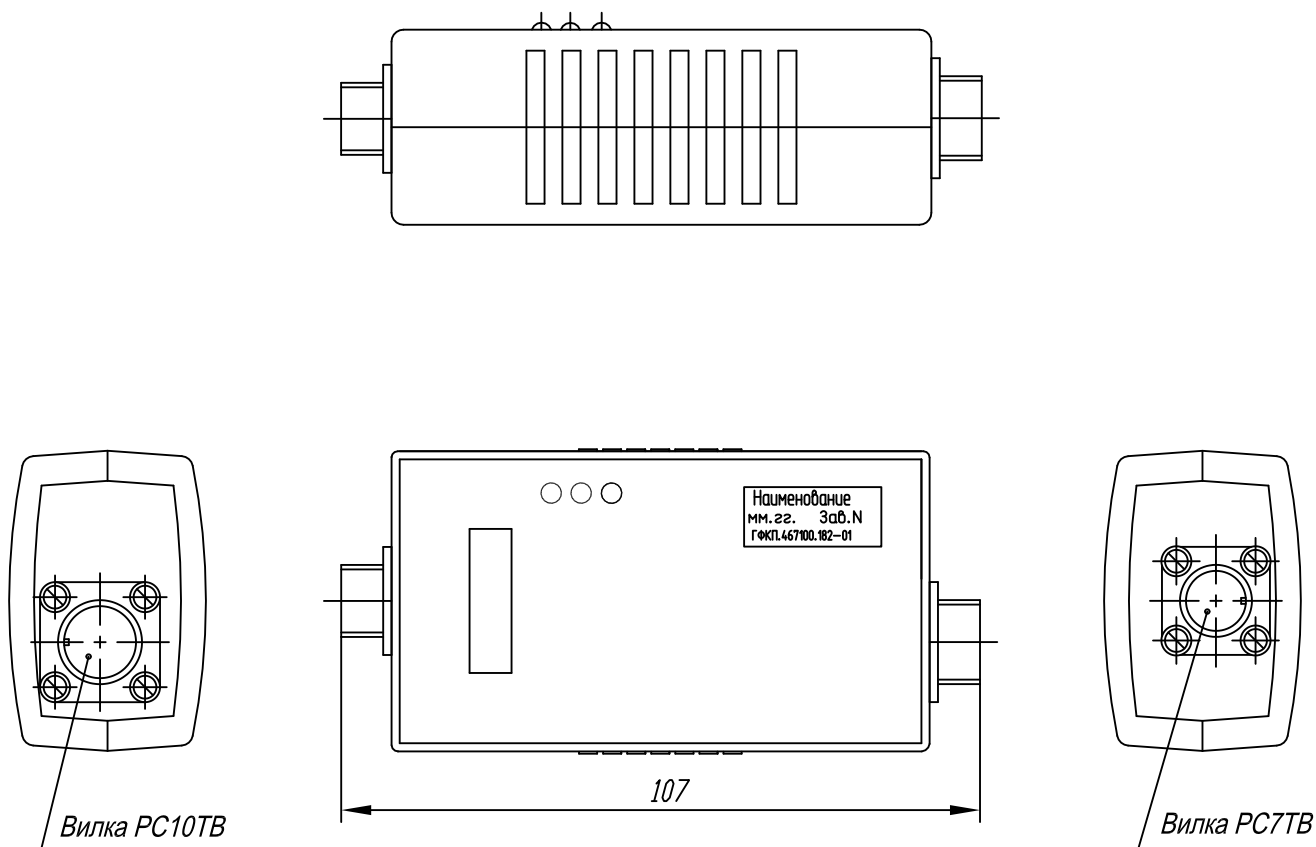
Габаритный чертеж модуля TA1-USB-01
